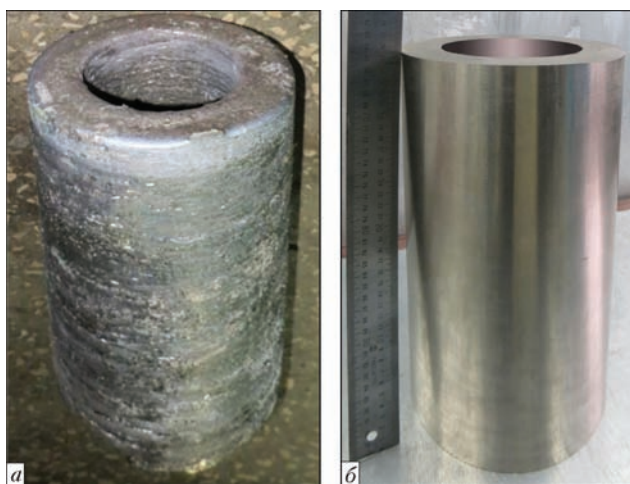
Внешний вид трубчатой заготовки, полученной способом ЭЛП, после выплавки (а) и механической обработки (б)
